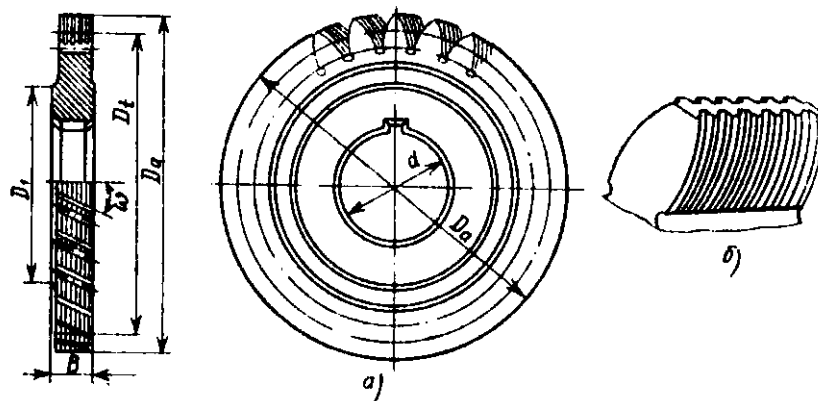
Дісковий шевер: а – конструктивні елементи б – зуб шевера.
